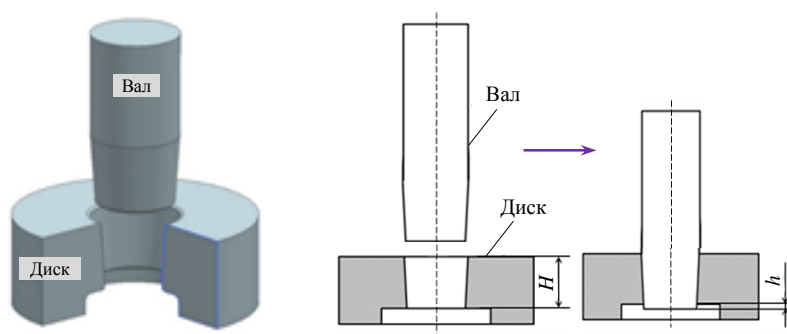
Общий вид образцов, имитирующих детали ГТД «диск + вал», и схема сварки давлением сплавов ЭК79 и ЭП975
